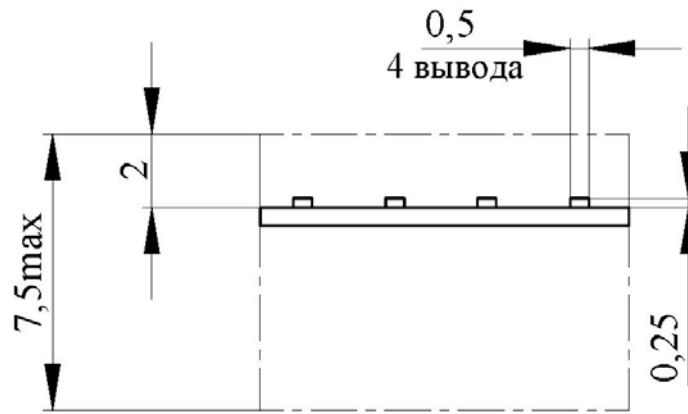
Габаритный чертеж модулей в конструктивном исполнении «Е»
